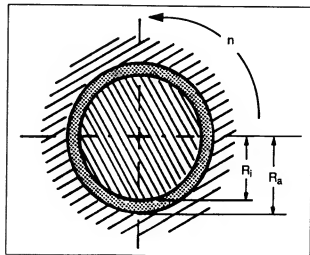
Поперечное сечение подшипника скольжения коленчатого вала с кольцевым зазором для смазки
